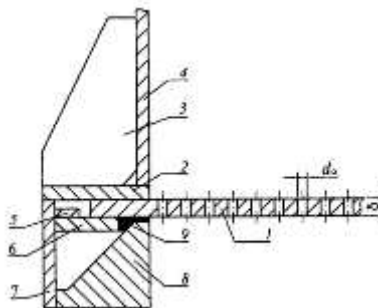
Крепление газораспределительной решетки: 1 – решетка; 2 – фланец; 3 – косынка; 4 – верхний корпус сушилки; 5 – ограничитель; 6 – опора; 7 – нижний корпус сушилки; 8 – футеровка; 9 – уплотнительная набивка (асбестовый шнур)
